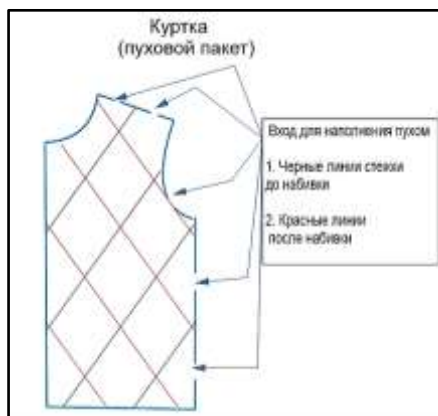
Схема пухового пакета и отверстий для набивки пухом
